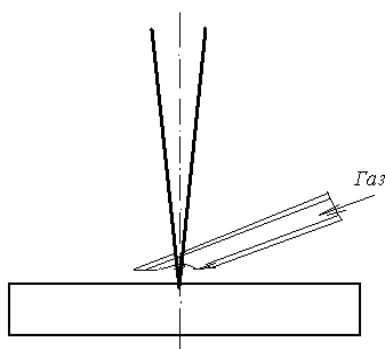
Применение защитных газов при лазерной сварке
